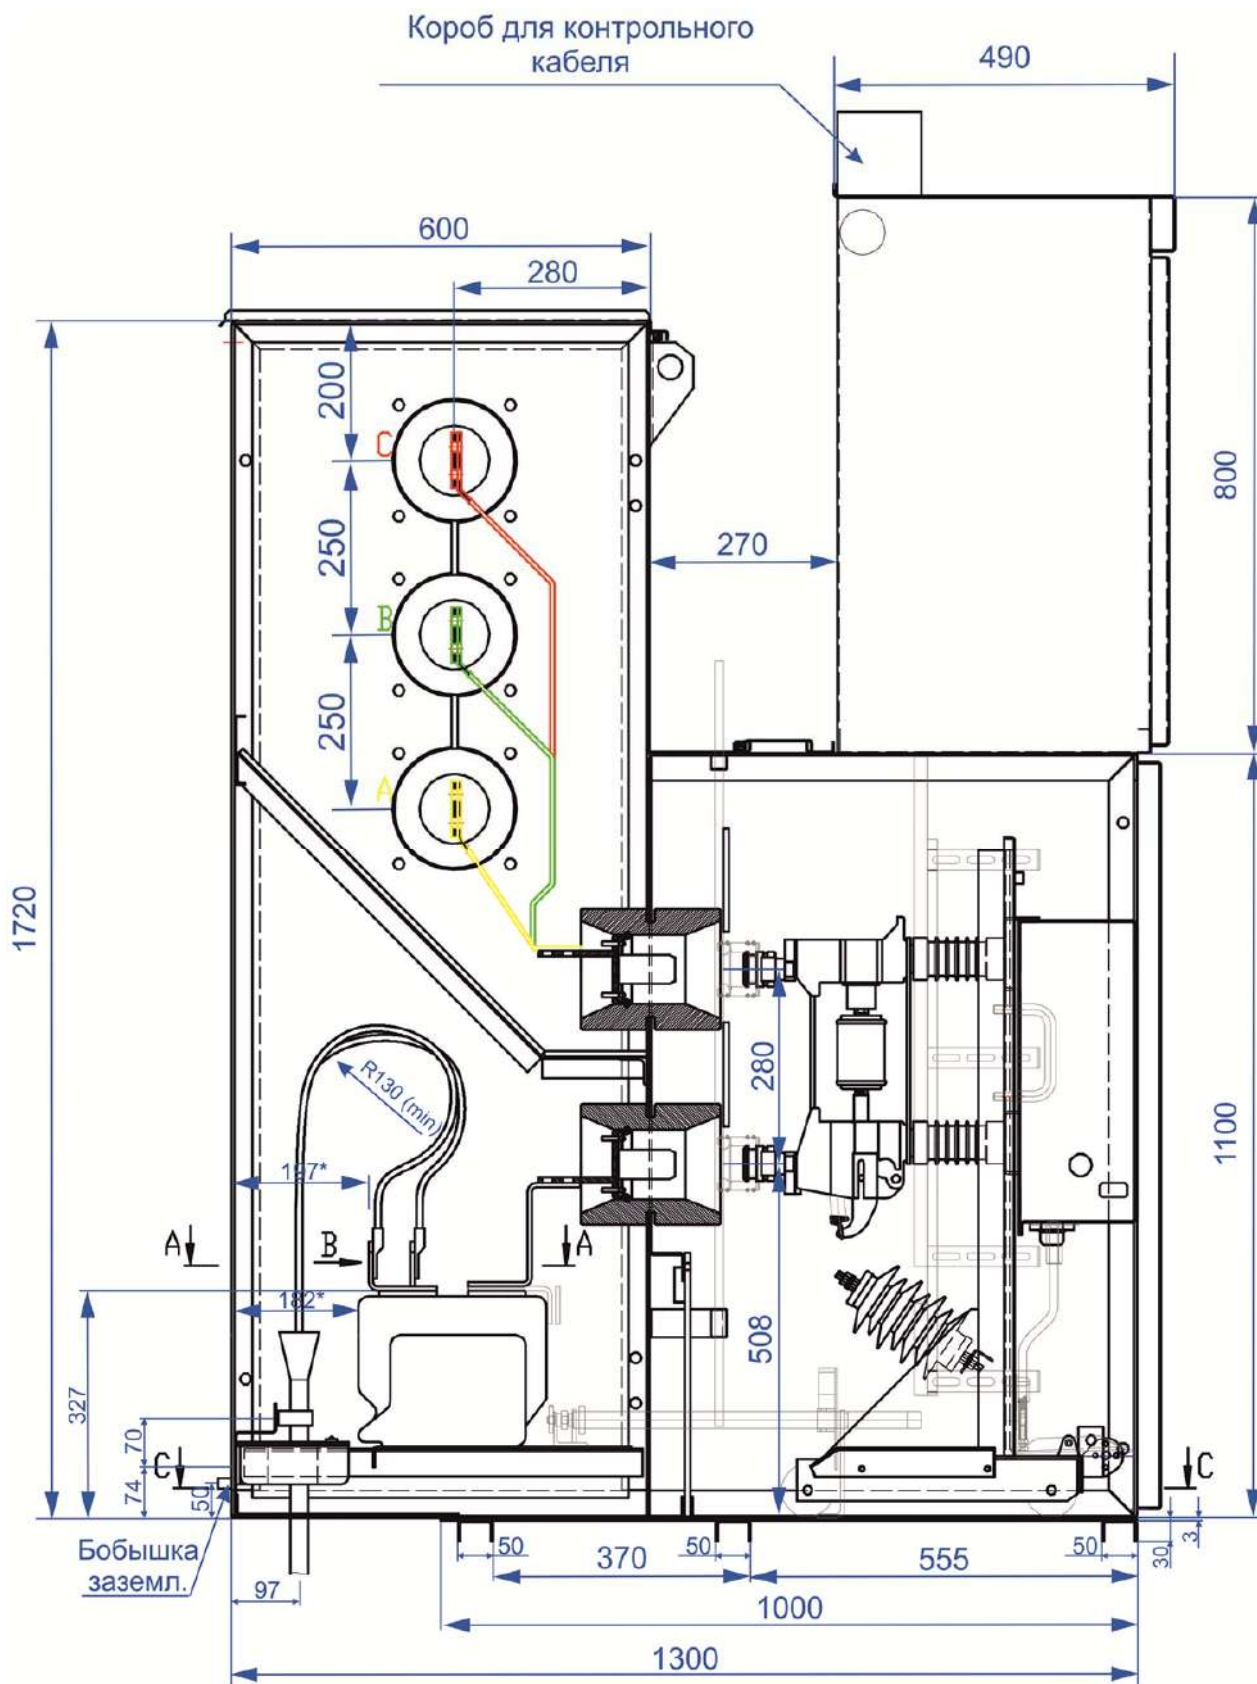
Габаритно-присоединительные размеры шкафа КМ-1КФ с вакуумным выключателем
